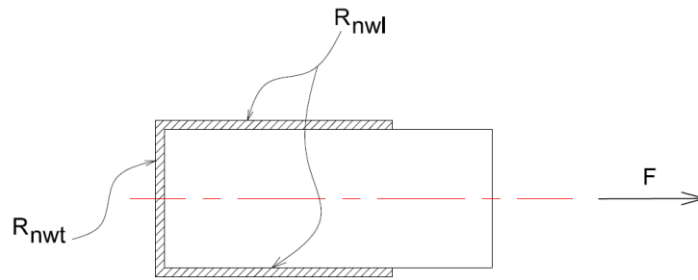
Soldadura transversal y longitudinal cargados concéntricamente
